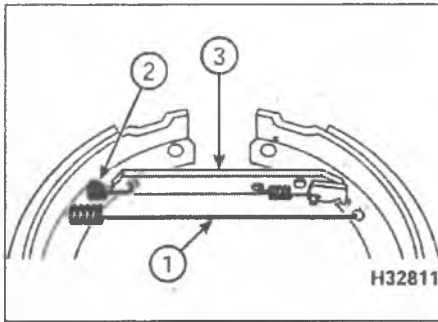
Верхняя возвратная пружина (1), пружина регулировочной планки (2) и регулировочная планка (3)
